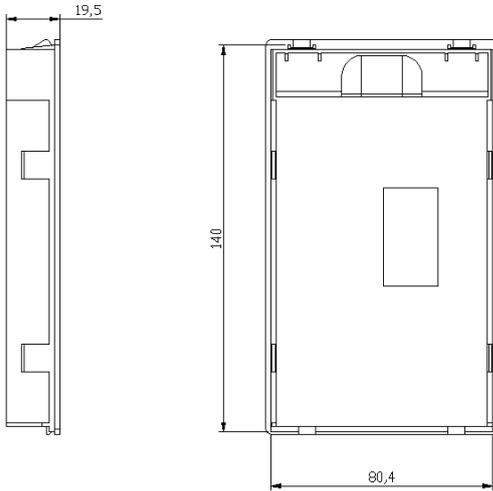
外引键盘支架外形尺寸图(单位 mm)
